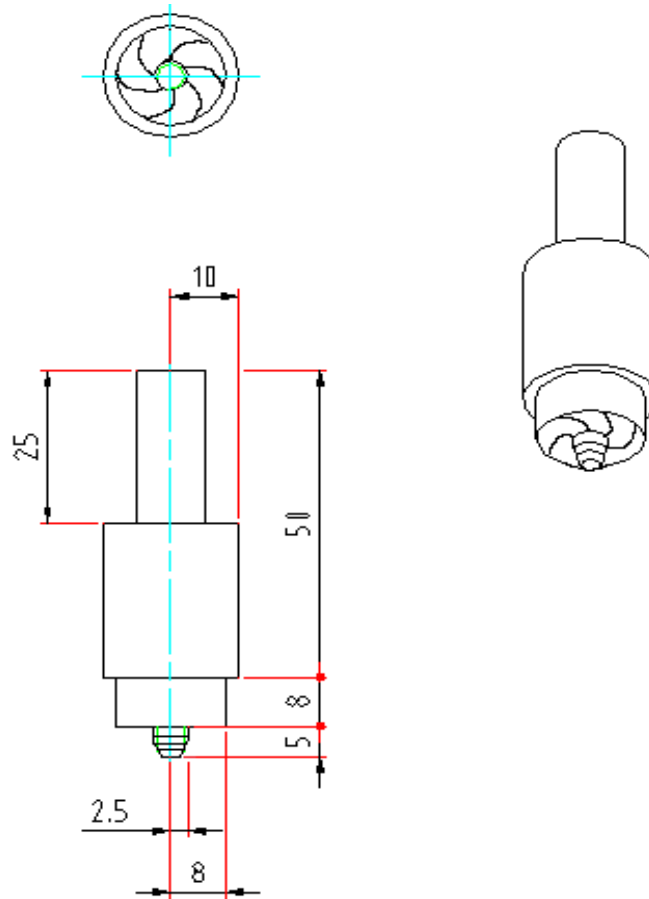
Segundo diseño de la herramienta para el Soldado por Fricción y Agitación
